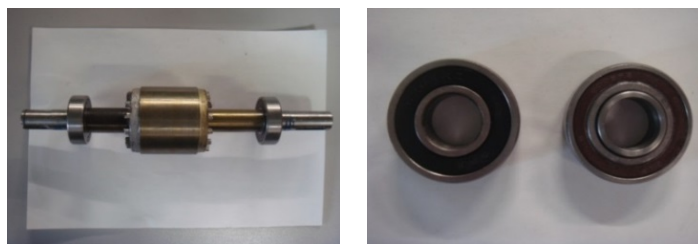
Ротор и подшипники АД: а – внешний вид ротора АД, б – заводской подшипник и подмененный подшипник с внутренней втулкой
